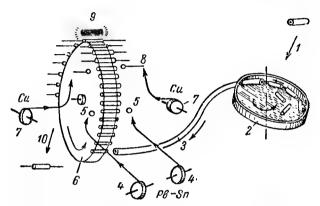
Схема автомата для пайки выводов к трубчатым заготовкам при изготовлении конденсаторов типа KTK.
